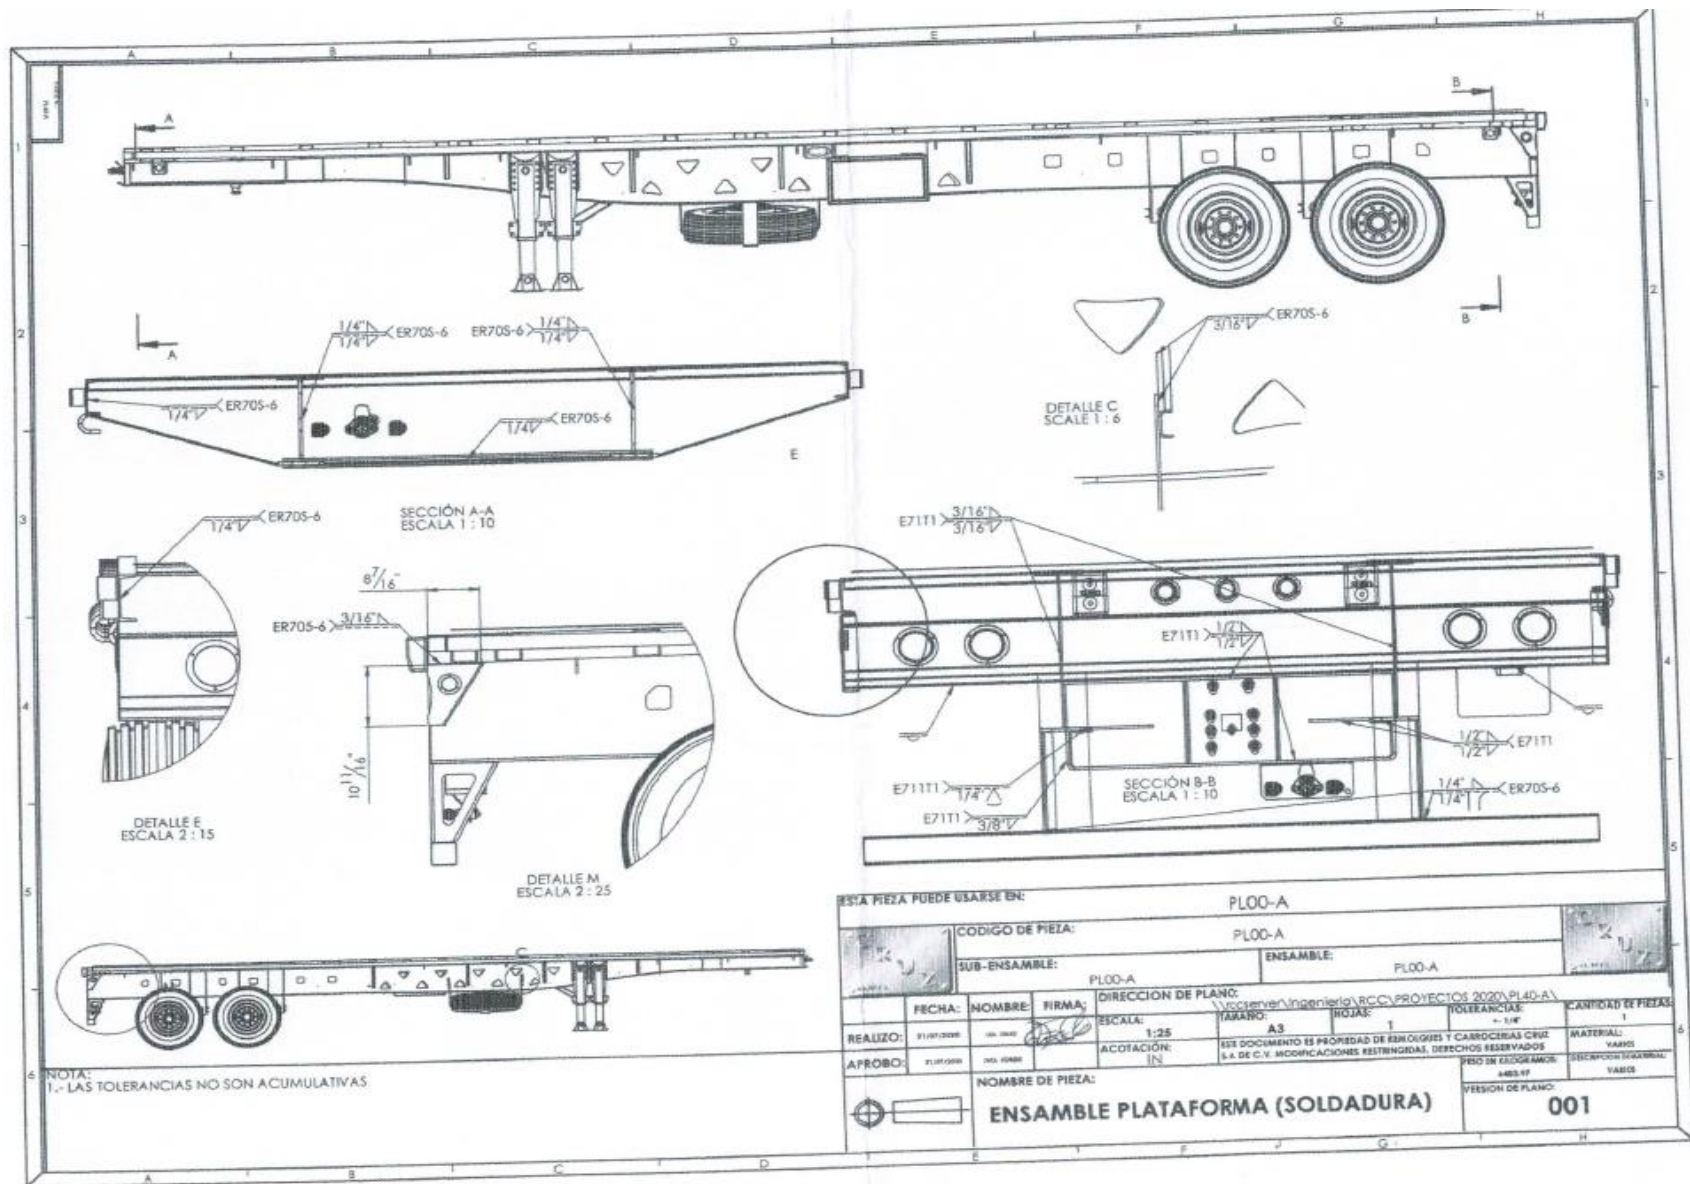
Plano del ensamble de plataforma (soldadura). Fuente: Remolques y Carrocerías Cruz, S.A. de C.V., 2020.
